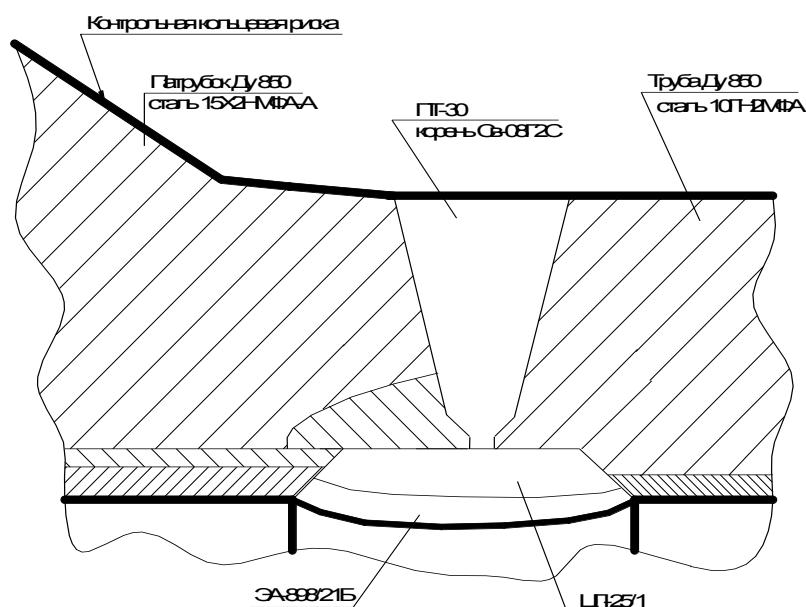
Монтажное СС трубы узла трубного с патрубком корпуса реактора
